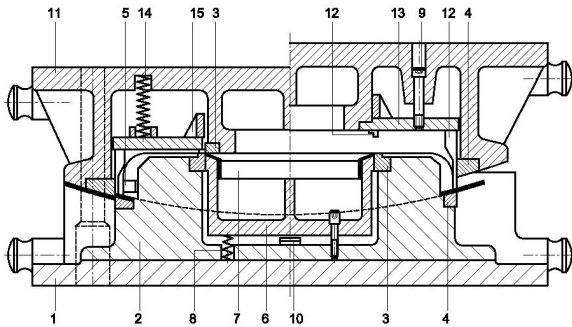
Beschneidwerkzeug - Großwerkzeug
